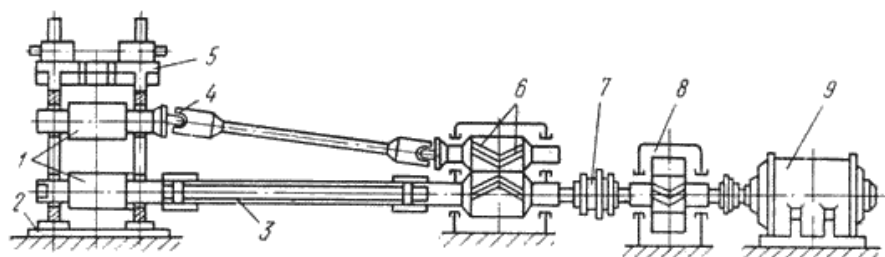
Схема головної лінії прокатного стану: 1 – прокатні валки; 2 – плита; 3 – тріфазний шпиндель; 4 – універсальний шпиндель; 5 – робоча кліть; 6 – шестеренна кліть; 7 – муфта; 8 – редуктор; 9 – двигун.
